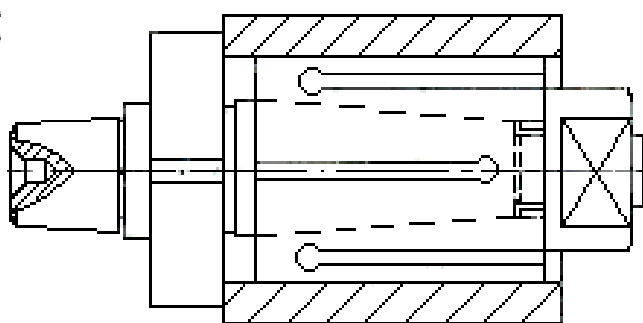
Установка заготовок на розтискній цанговій оправці
